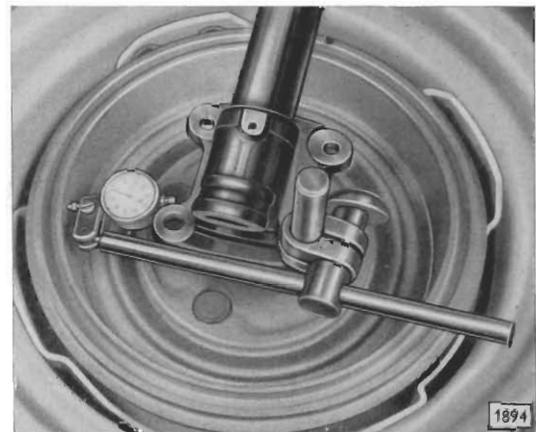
Vorderrad-Bremstrommel mit angeschraubtem Rad auf Rundlauf prüfen
